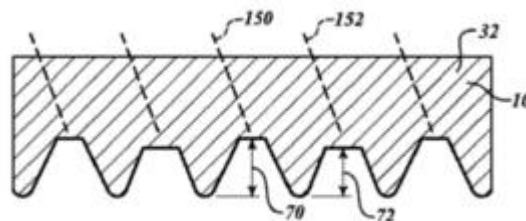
Витки зубьев на цилиндрическом корпусе фрезы
